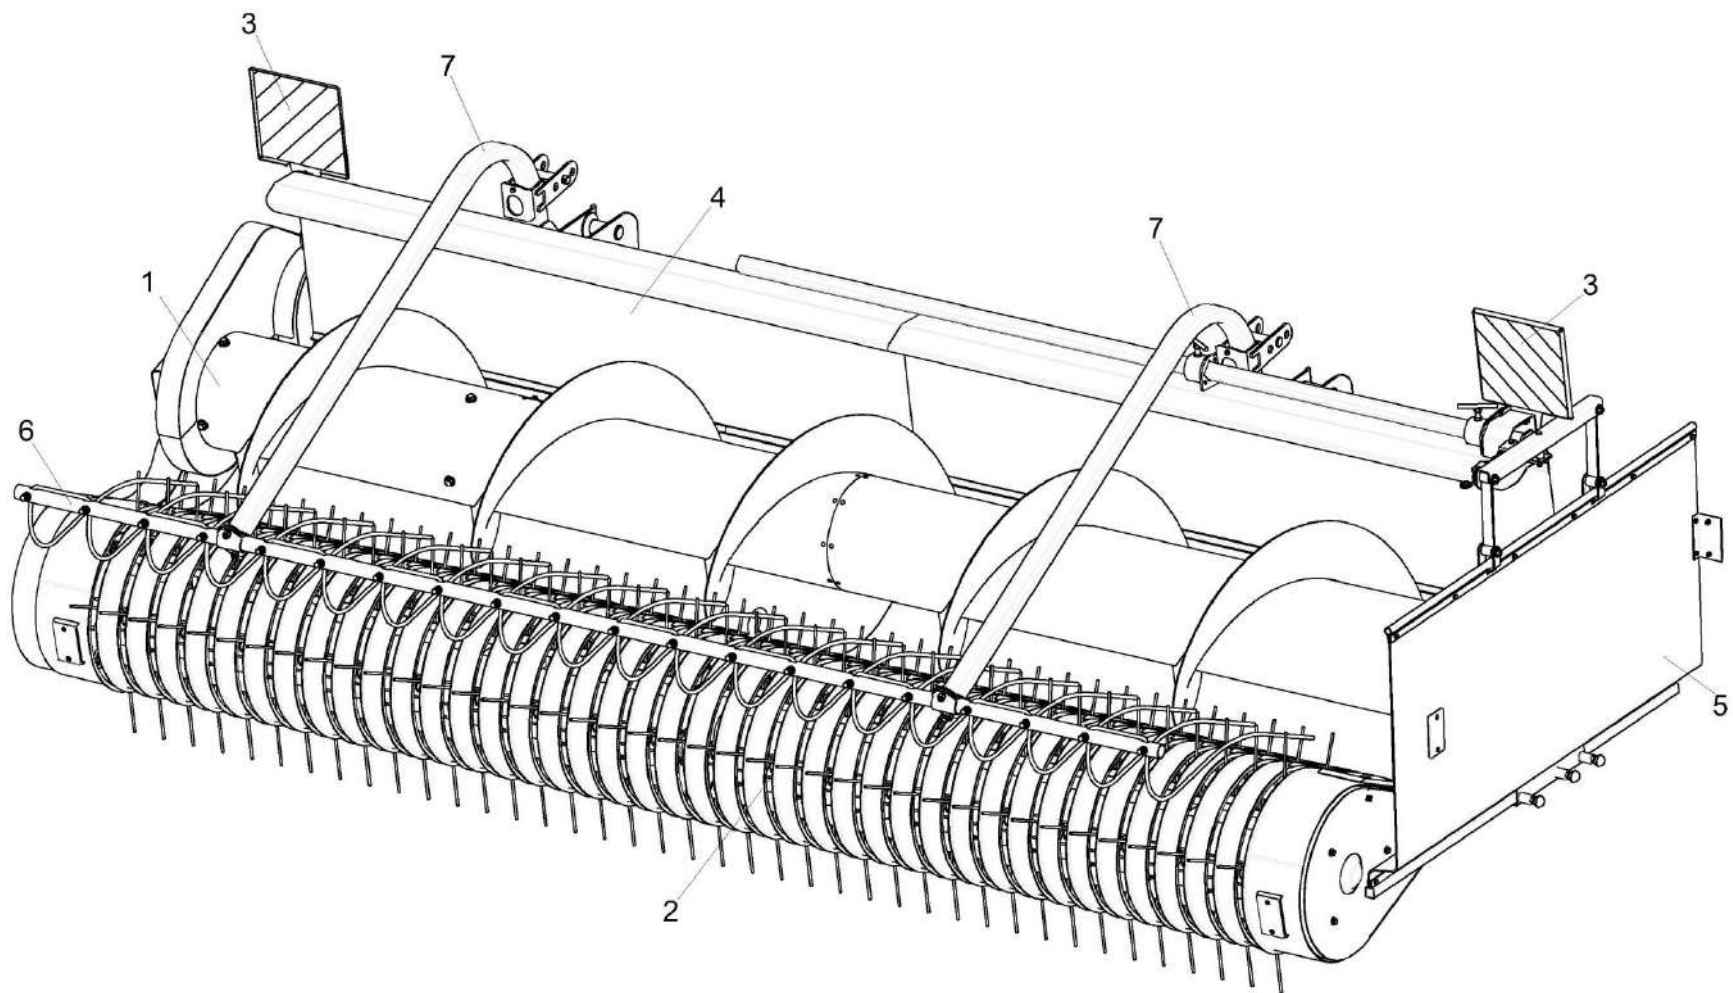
Валкооборачиватель КС-100-4900000 (общий вид)
